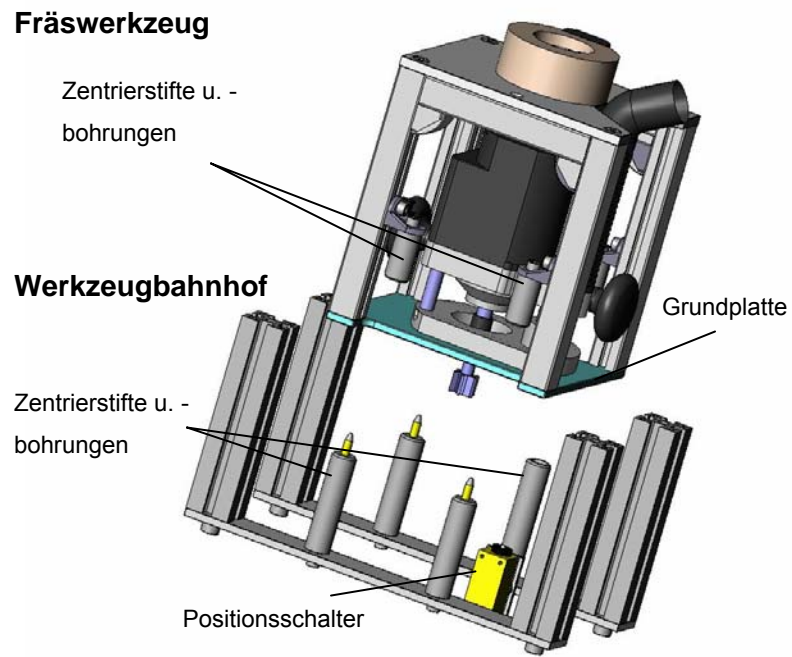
Werkzeugbahnhof mit Fräswerkzeug
